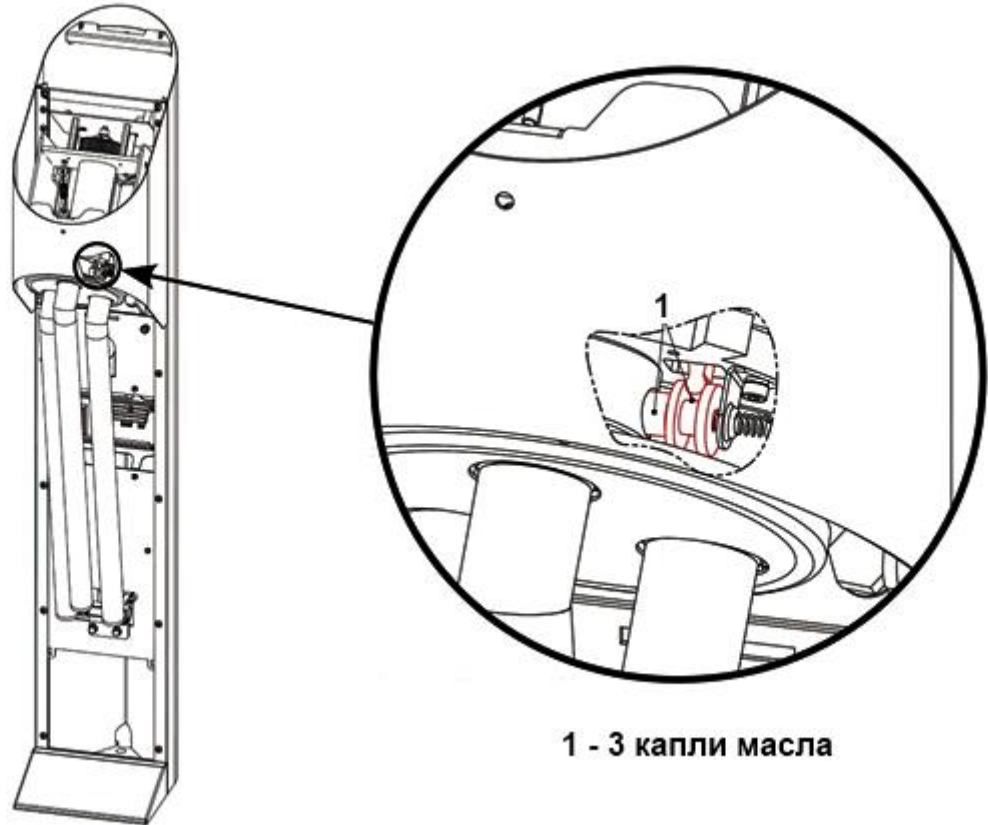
Места соединения фиксатора и кулачка разблокировки планок
